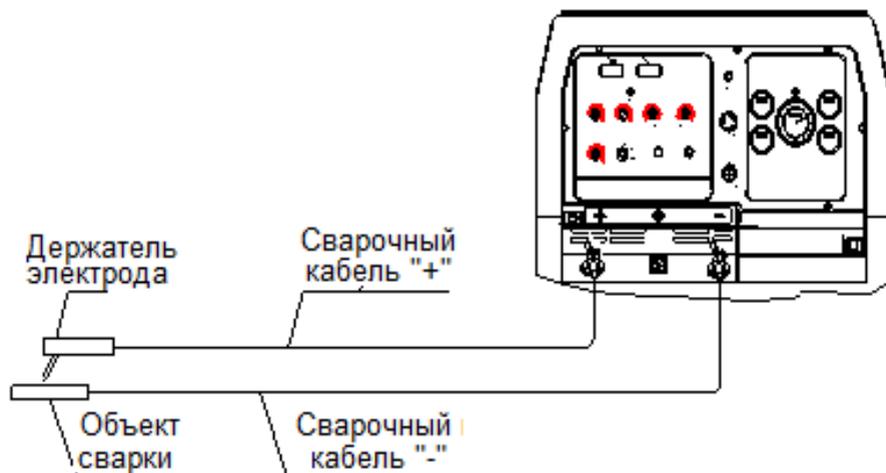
Схема подключения при сварке покрытым электродом (MMA)
